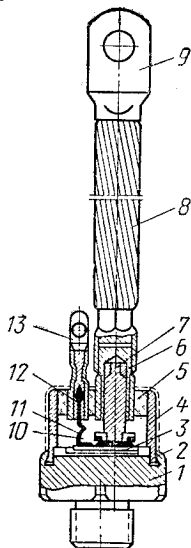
Управляемый кремниевый вентиль — тиристор в разрезе.
